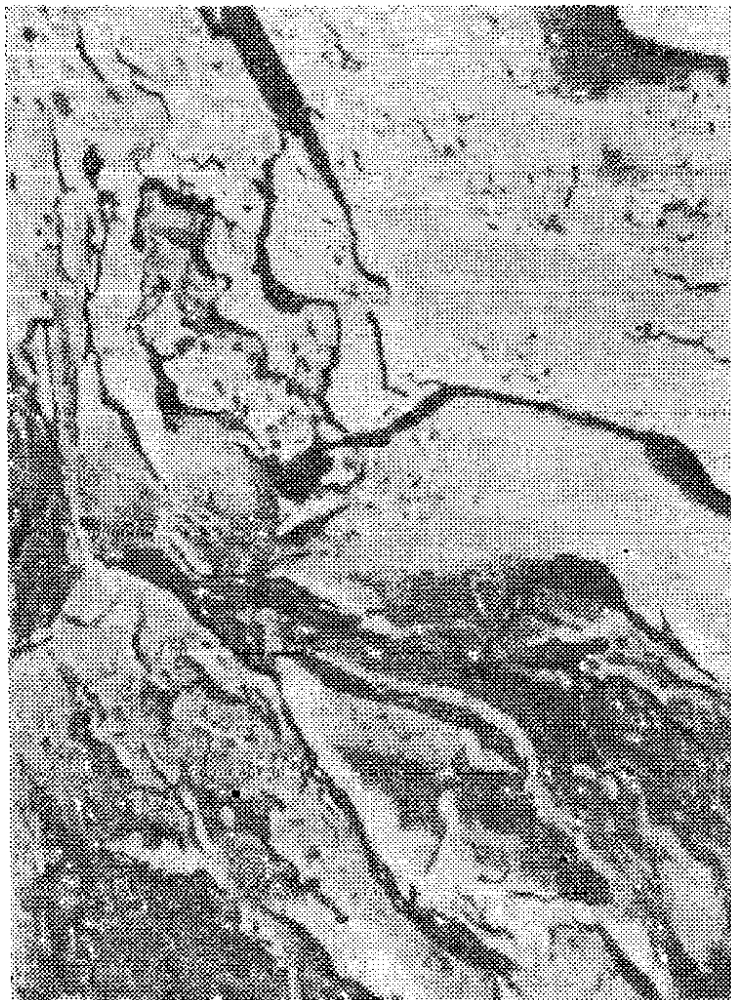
Поверхности разрушения левой отливки представляют собой типичную поверхность хрупкого разрушения отрывом без признаков усталости или коррозии. Увеличение 6 тыс. раз
